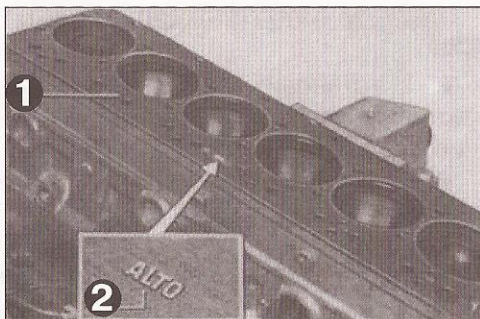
Расположение прокладки головки блока цилиндров при установке.
